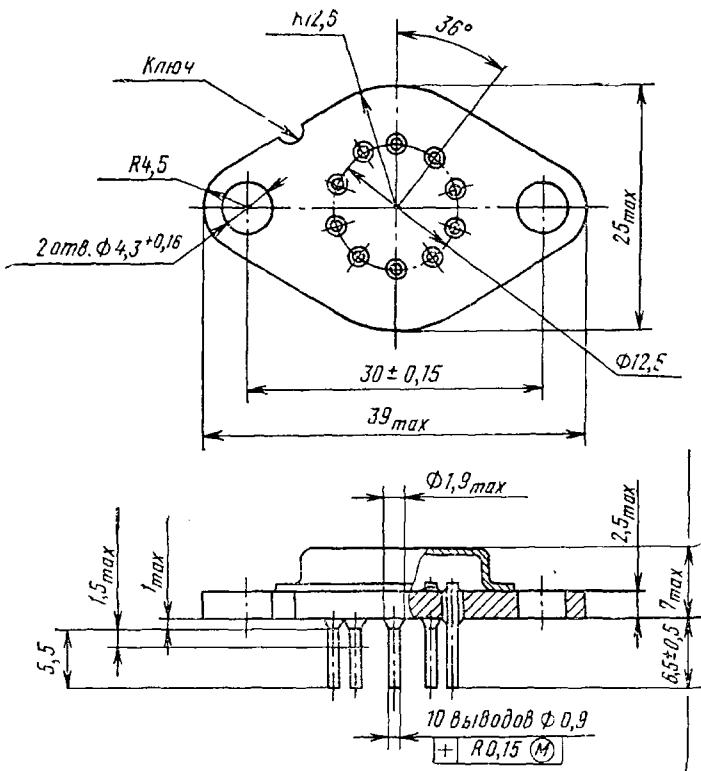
Конструкция металлостеклянного корпуса 3204 (311.10-1)
